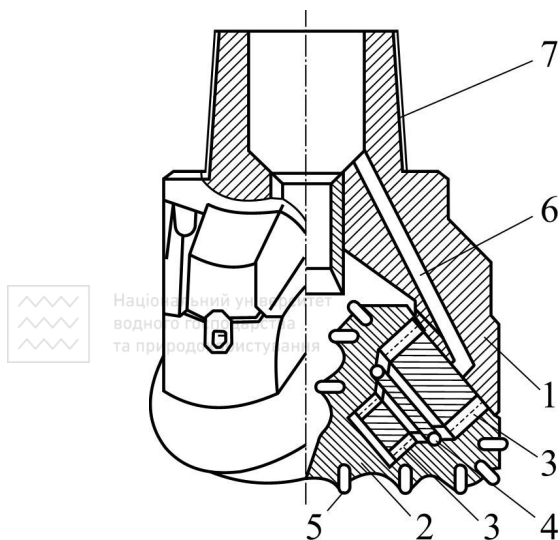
Конструкція трюхшарошечного долота: 1 – лапа; 2 – шарошка; 3 – роликовий підшипник; 4 – кульковий підшипник; 5 – штирі із твердого сплаву; 6 – канал для подачі стисненого повітря; 7 – нарізний ніпель
